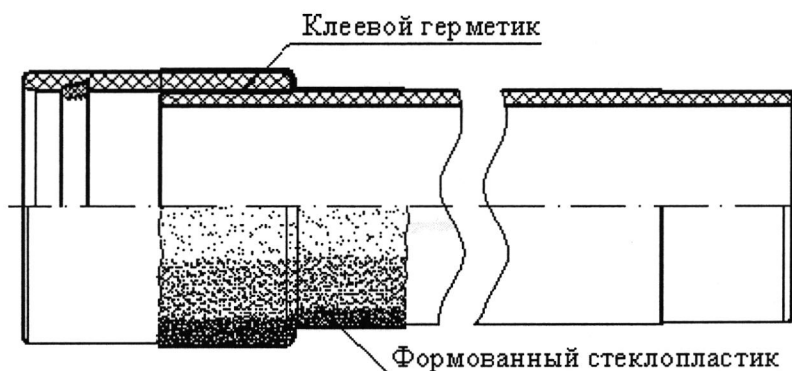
Поставка труб с закрепленным раструбом из заготовки муфты и уплотнителем.
